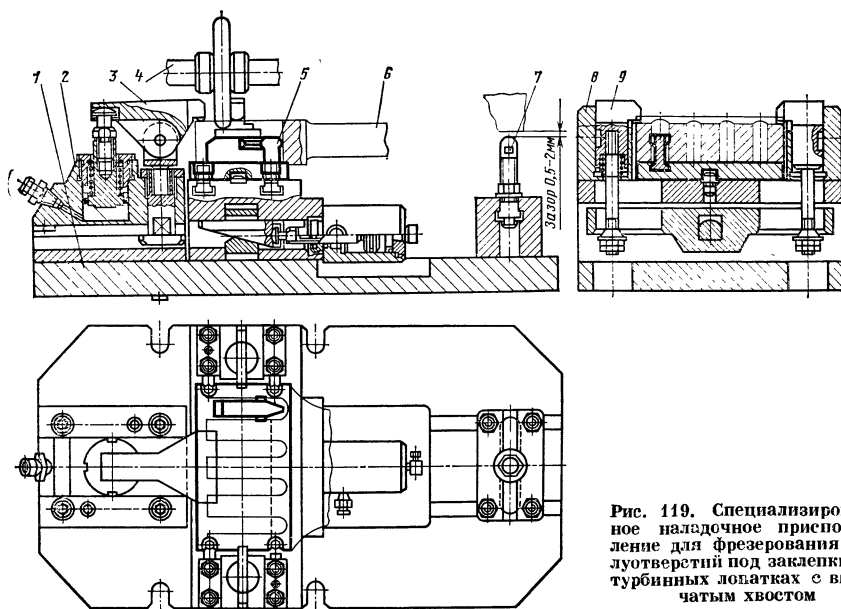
Специализированное наладочное приспособление для фрезерования полуотверстий под заклепки на турбинных лопатках с вильчатым хвостом
